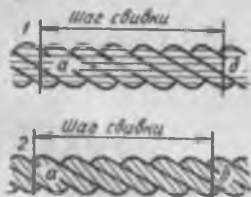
Определение шага свивки каната: 1 — крестовой свивки; 2 — односторонней свивки
